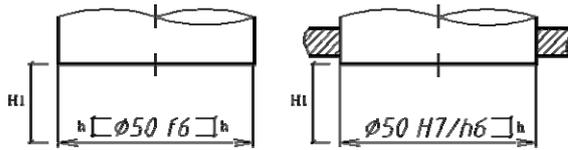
Acotación con tolerancias indicadas por símbolos ISO. (Ejemplos con h = 5 mm).
